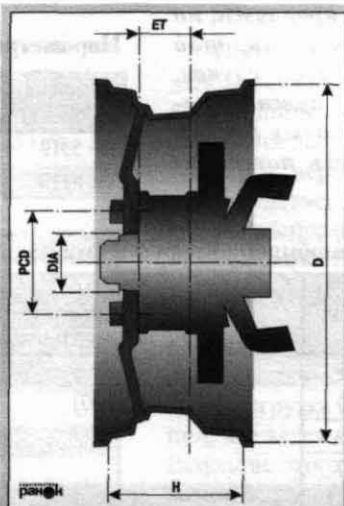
Основные размеры и параметры колесного диска: D – посадочный диаметр обода; H – посадочная ширина обода; ET – вылет обода; PCD – диаметр расположения крепежных отверстий; ЦО (DIA) – диаметр центрального отверстия
